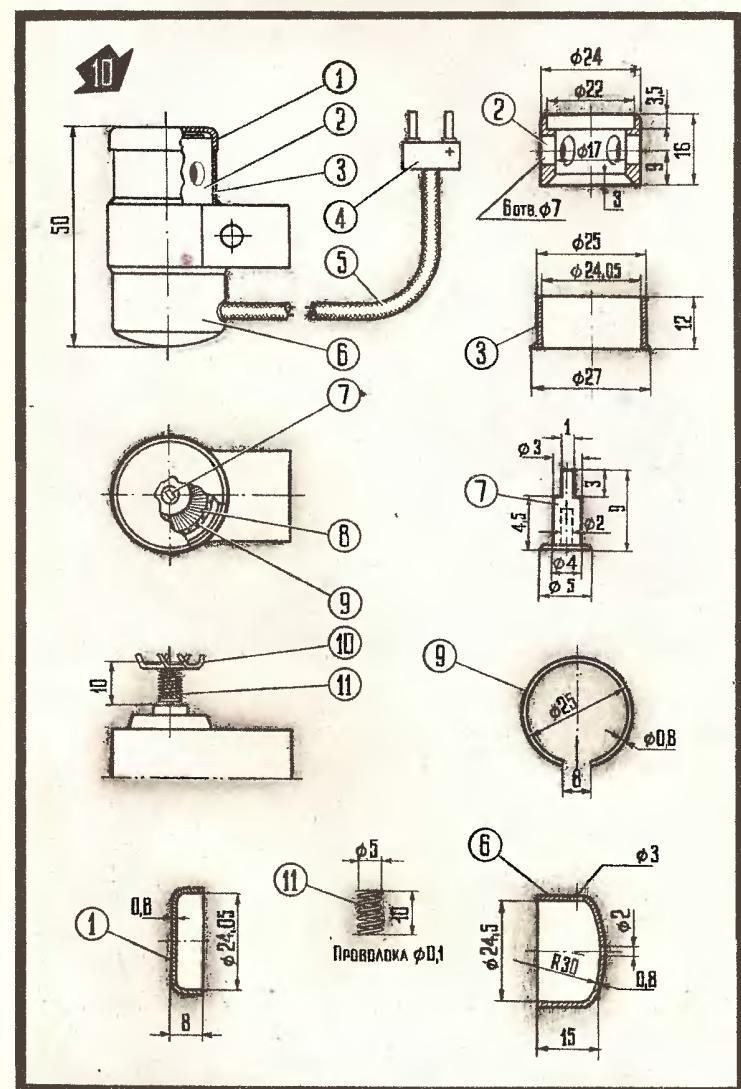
Бритва в сборе и ее детали: 1 — крышка; 2 — опорное кольцо из органического стекла, которое прикрепляется к корпусу двигателя kleem БФ-2; 3 — защитное dioraluminиневое кольцо, надеваемое на опорное кольцо (скользящая посадка); 4 — вилка; 5 — провод; 6 — крышка двигателя; 7 — наконечник оси двигателя (прикрепляется к оси kleem БФ-2); 8 — неподвижный нож (направляющая бритвы типа «Харьков»); 9 — стопорное кольцо неподвижного ножа; 10 — подвижный (вращающийся) нож; 11 — поджимная пружина.
